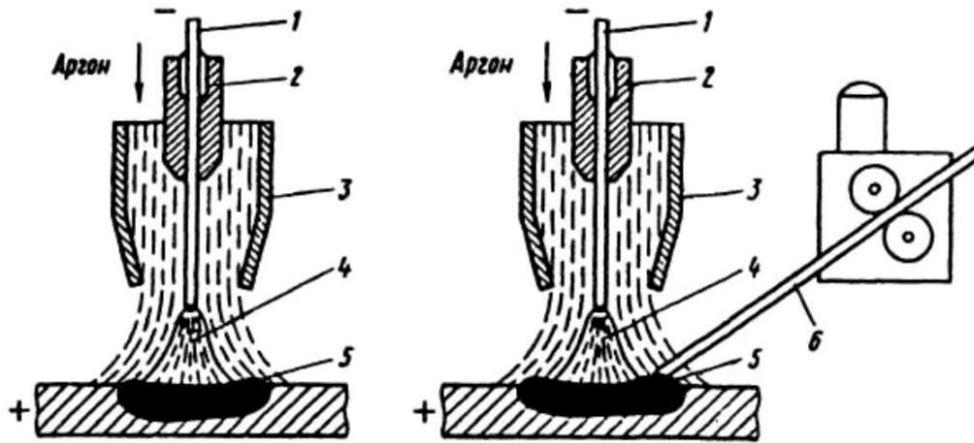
Схема зварювання неплавким електродом (TIG-зварювання)
